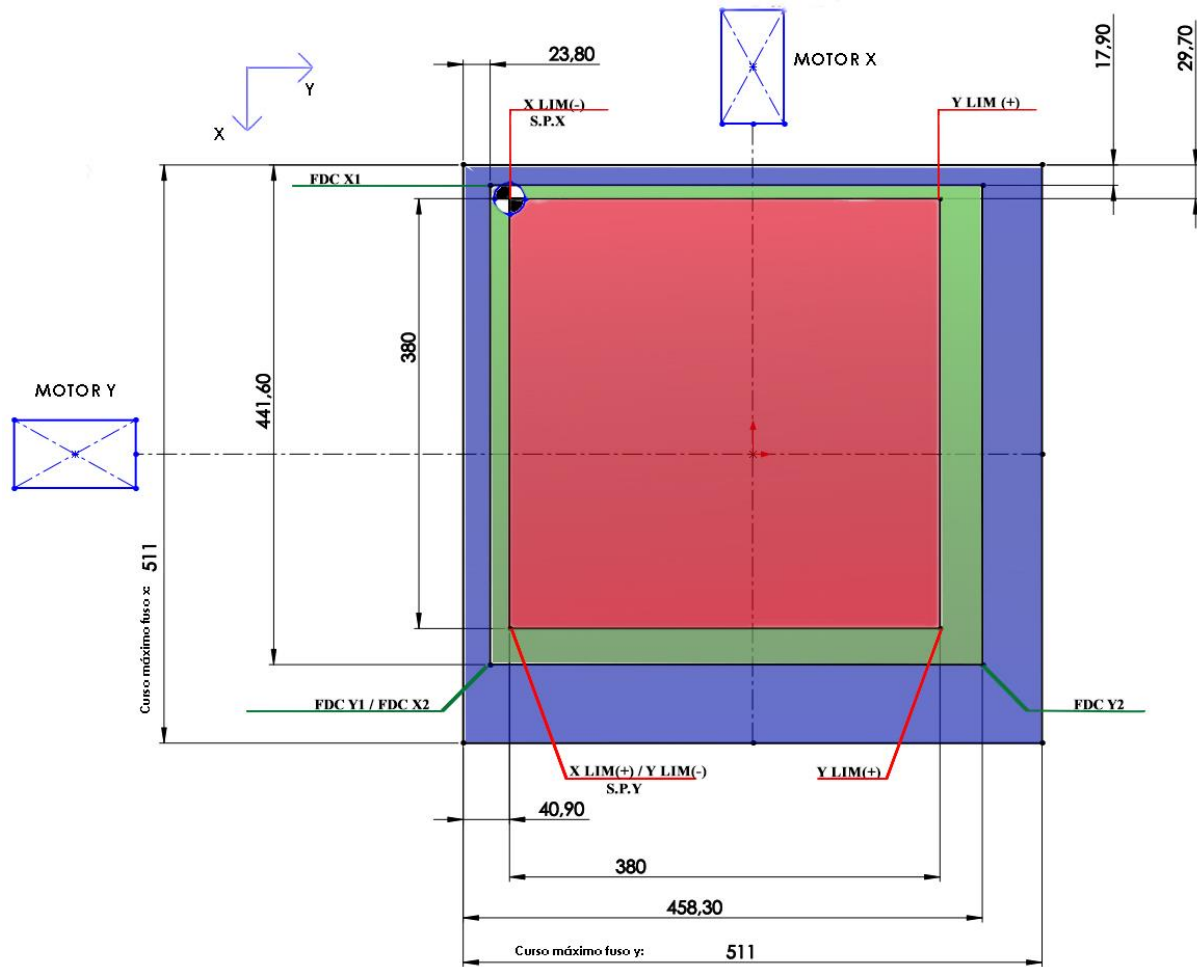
Configuração da área de trabalho (dimensões em mm)
